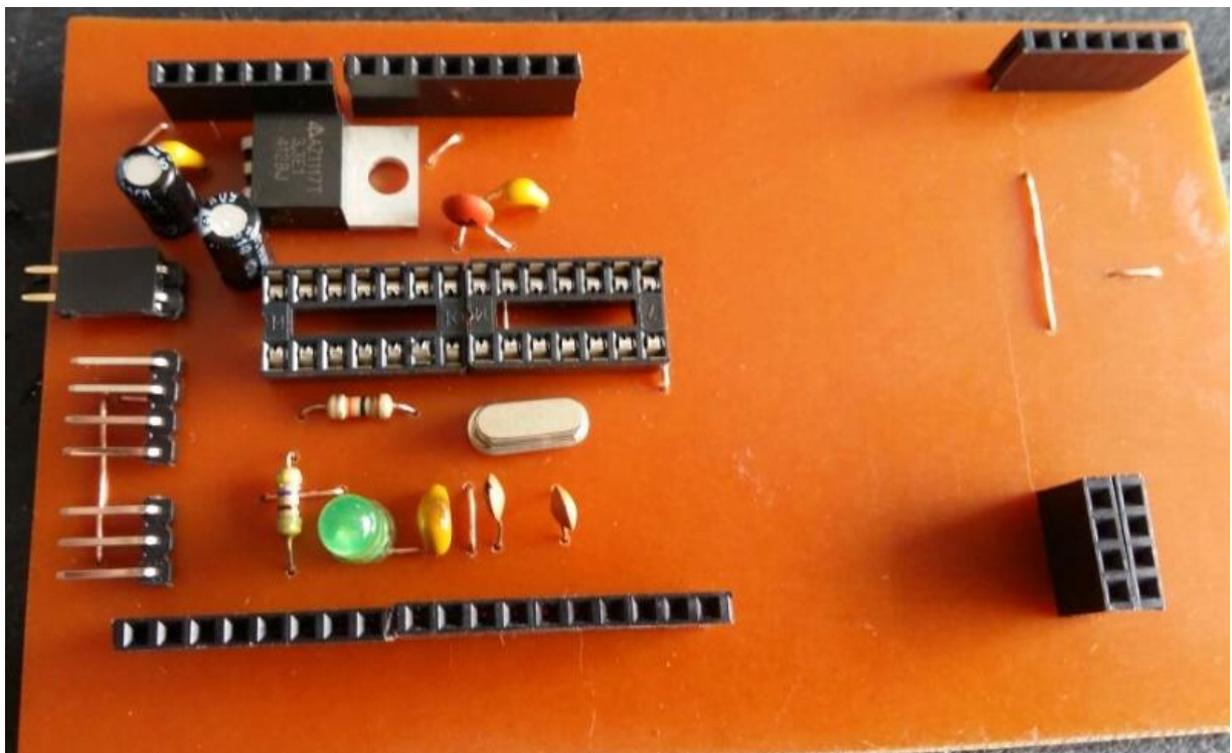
Montaje de elementos en la placa. (El Autor, 2018)
